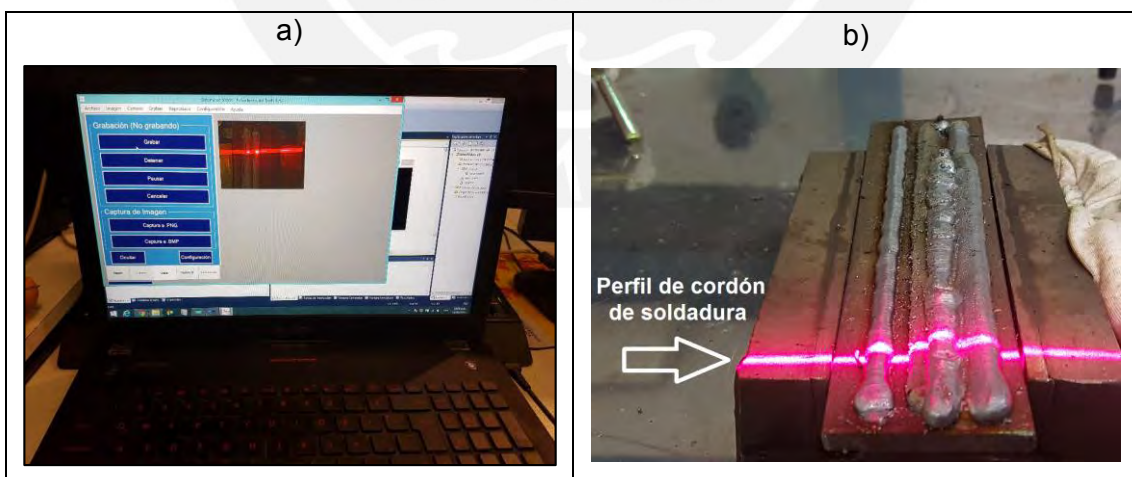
(a) Software de control y (b) perfil láser generado del cordón de soldadura del sistema de sensado híbrido
